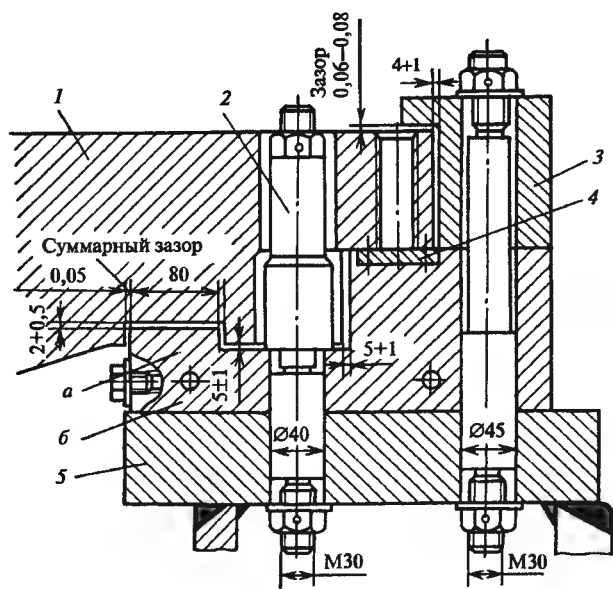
Узел сопряжения лапы и корпуса подшипника в турбине Т-250/300-23,5 ТМЗ:
